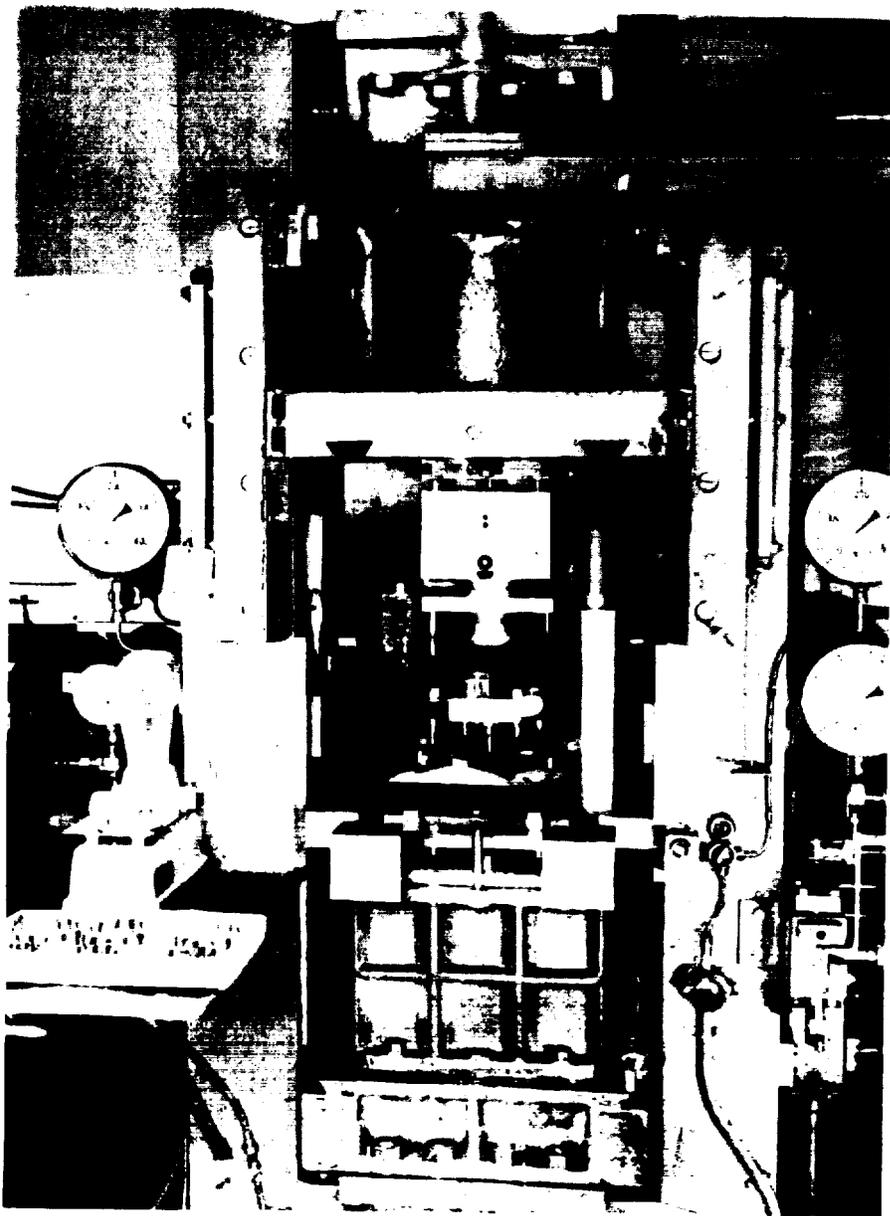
Maschinelle Sinterpresse für die Fertigung von FERROMET-Sinterformteilen
